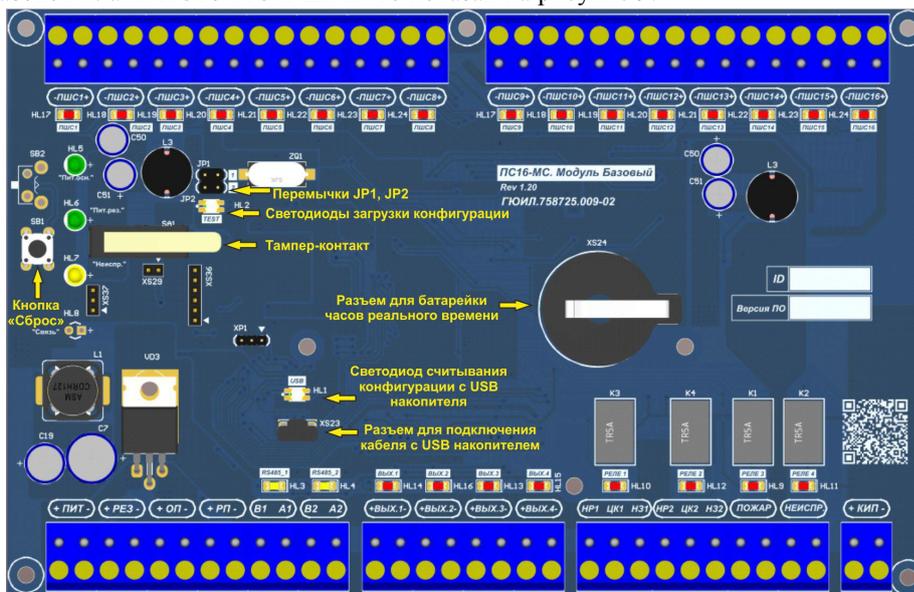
Внешний вид базовой платы ПС16-МС и ШМР16
